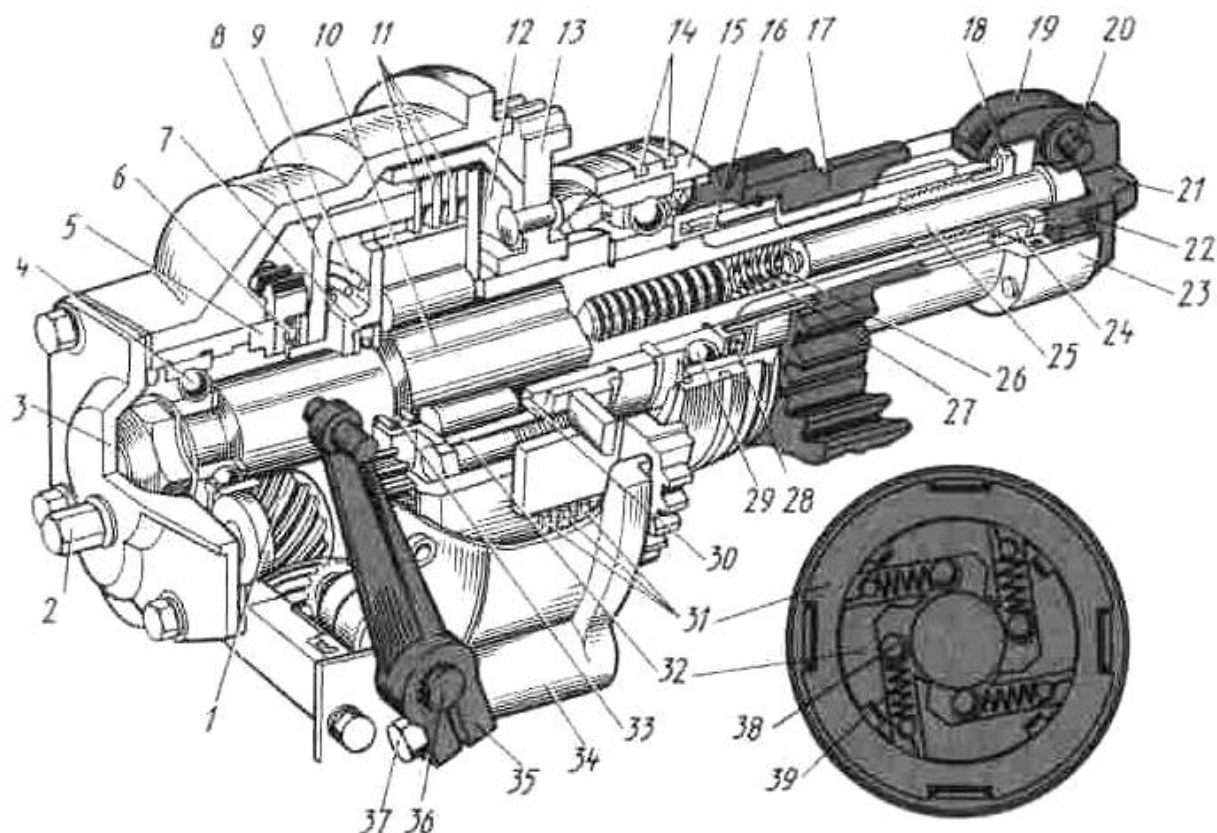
Редуктор 350.12.010.00 пускового двигателя дизелей типа СМД-60:
